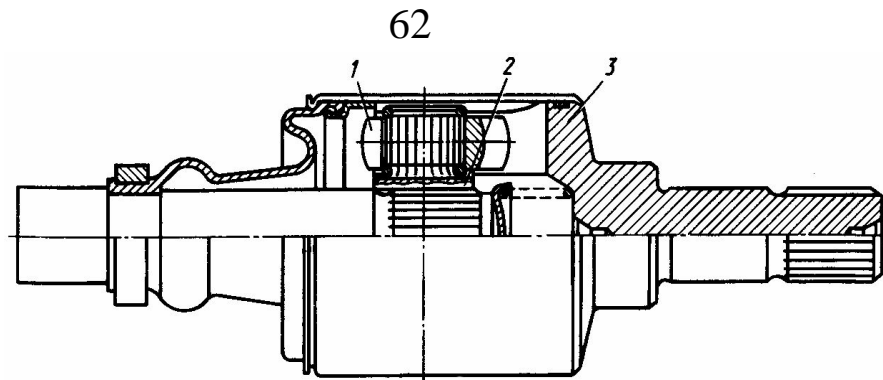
Универсальный трехшиповой карданный шарнир
